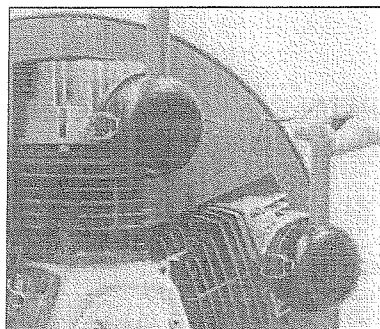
Крепление концевой пластины и защитного элемента ремня на обратной стороне кожуха охлаждающего воздуха
